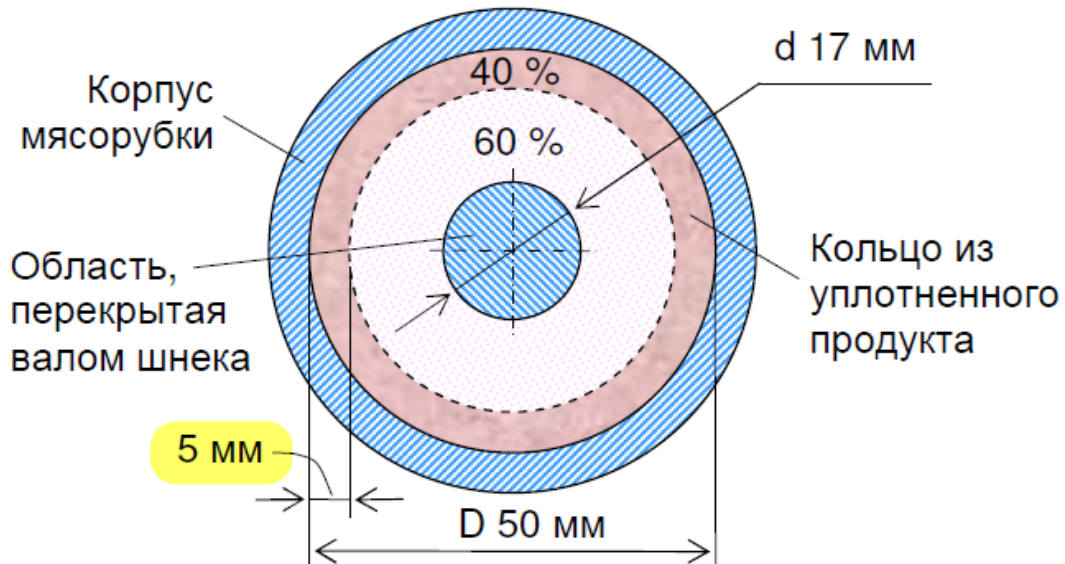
Уменьшение проходного сечения корпуса перед решеткой
